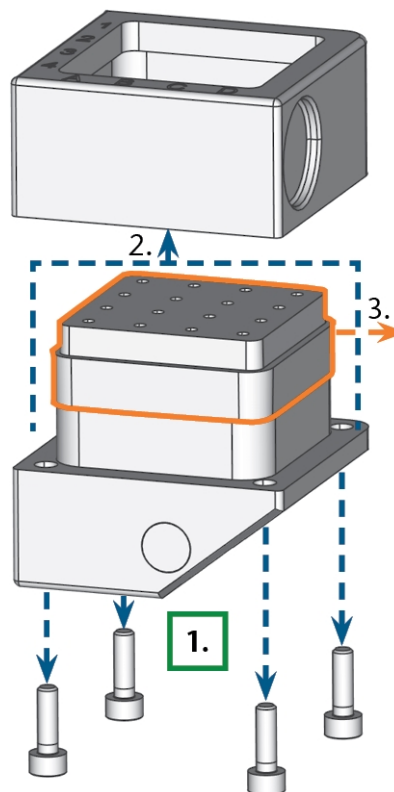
SMONTAGGIO DEL MAGAZZINO UTENSILI E RIMOZIONE DELL'INSERTO
